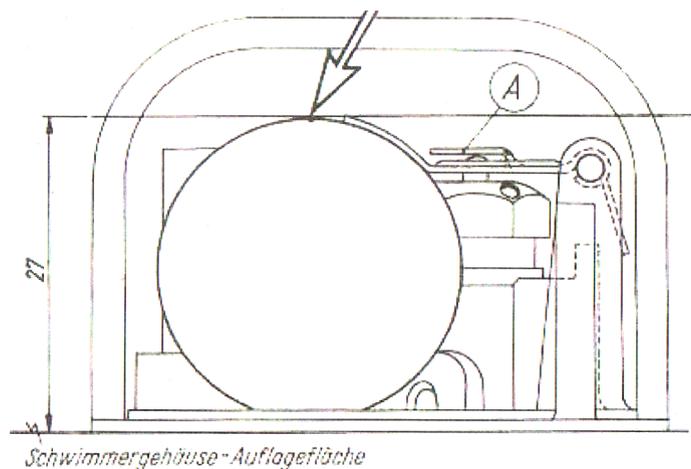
Schwimmerventil geschlossen. Federbolzen eingedrückt. A = Ventilhebel
